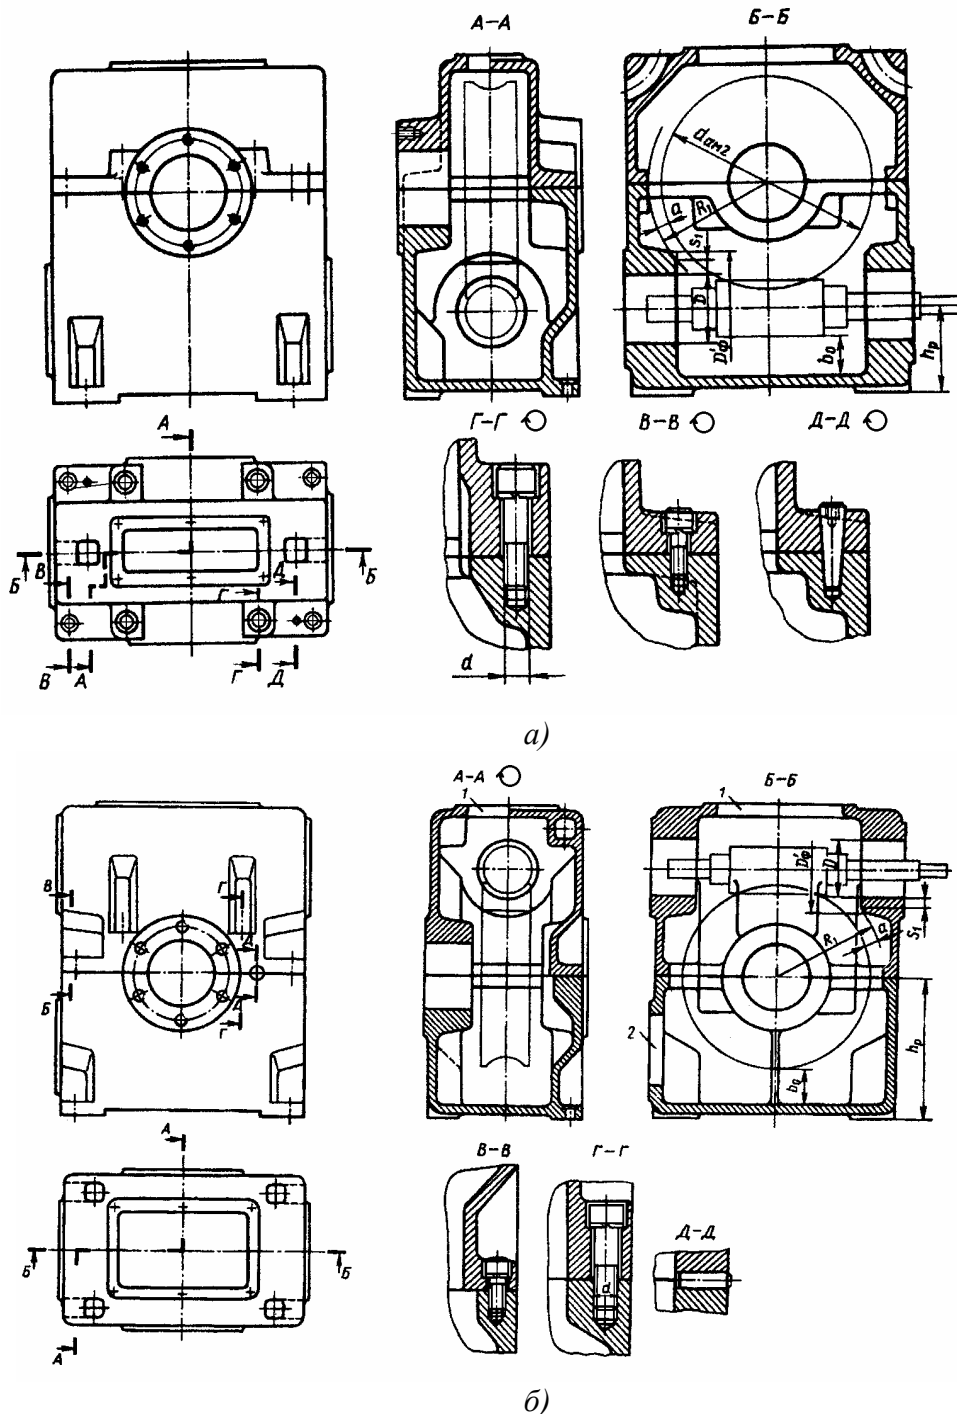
Современные конструкции разъемных корпусов червячных редукторов: а – с нижним; б – с верхним расположением червяка
